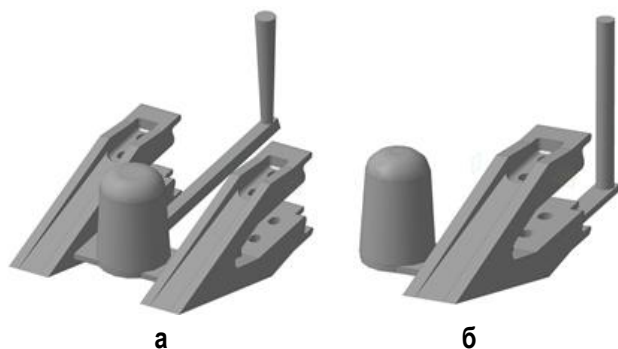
Отливка «Зуб ковша»: а – вариант 1; б – вариант 2
